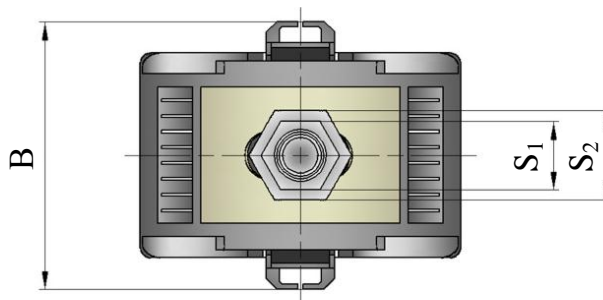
Габаритные и присоединительные размеры зажима ЗПО 1,5-10.
